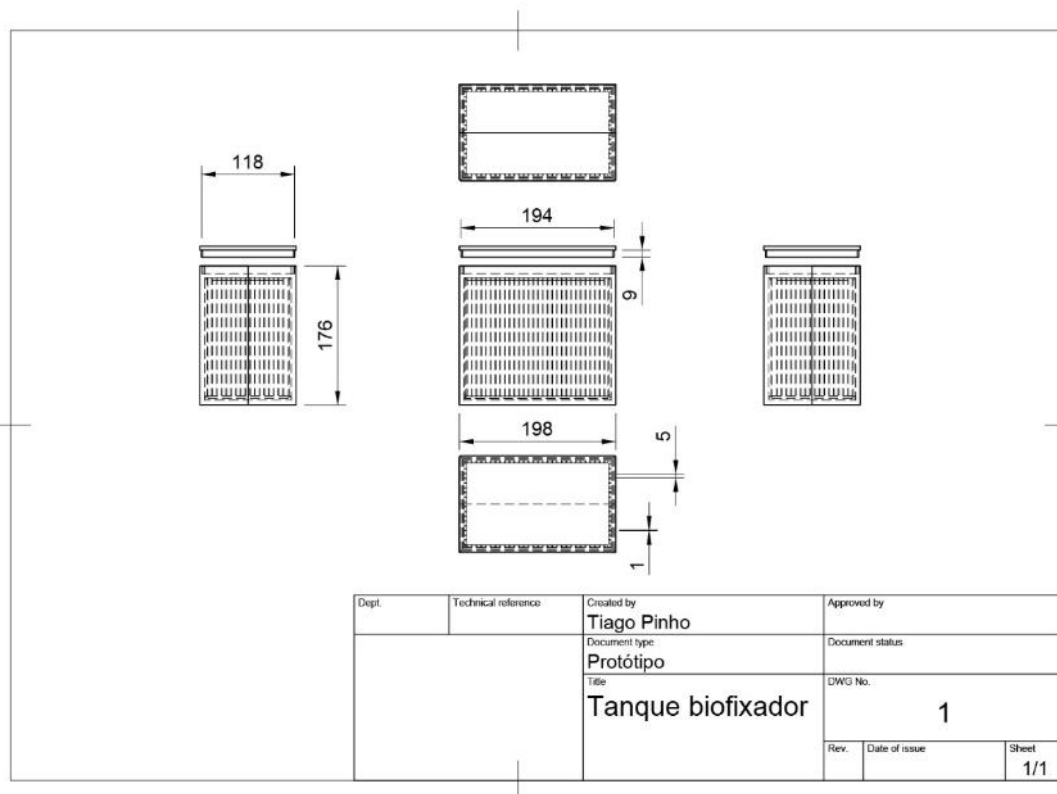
Desenho técnico do Tanque para o Ecofixador
